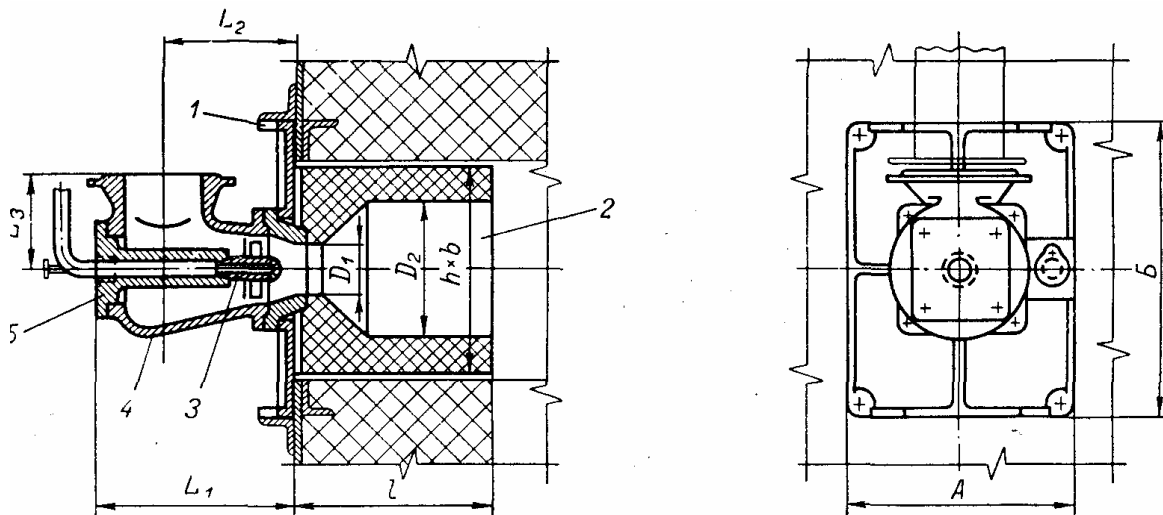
Горелка типа ГНП-1÷ГНП-9:
